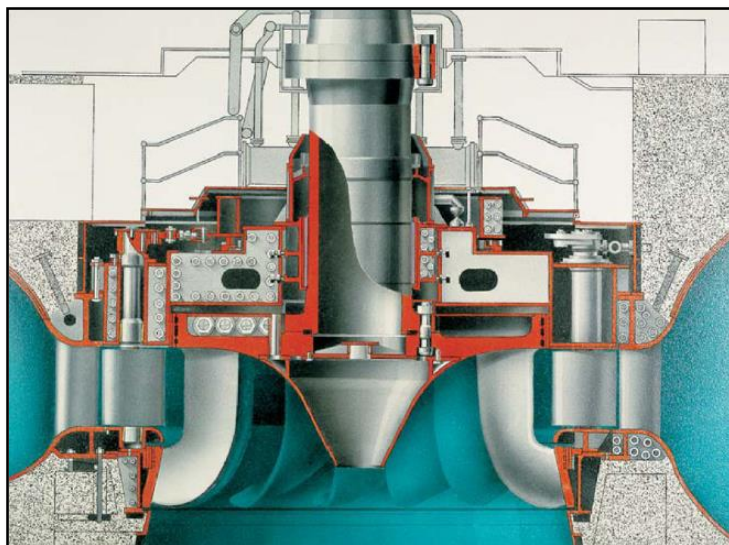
Vista em corte de uma Turbina Francis (Power Machines, 2004)
